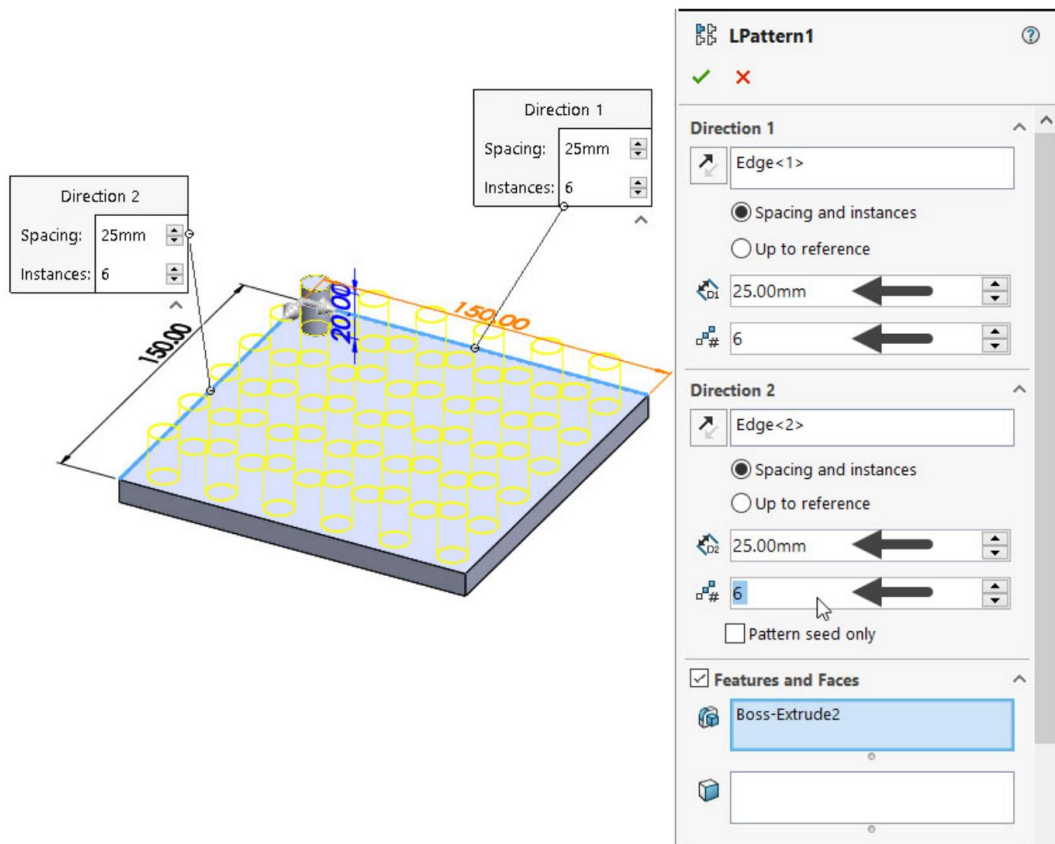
Налаштування для копіювання елемента циліндричного виступу за допомогою інструмента лінійний масив (Linear Pattern)
